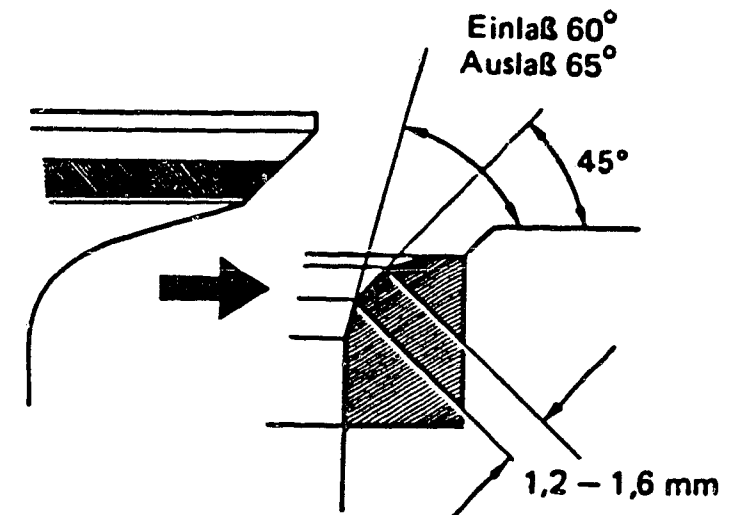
Motor 21R/21R-C: Bearbeitungsmasse und -winkel am Ventilsitz.
